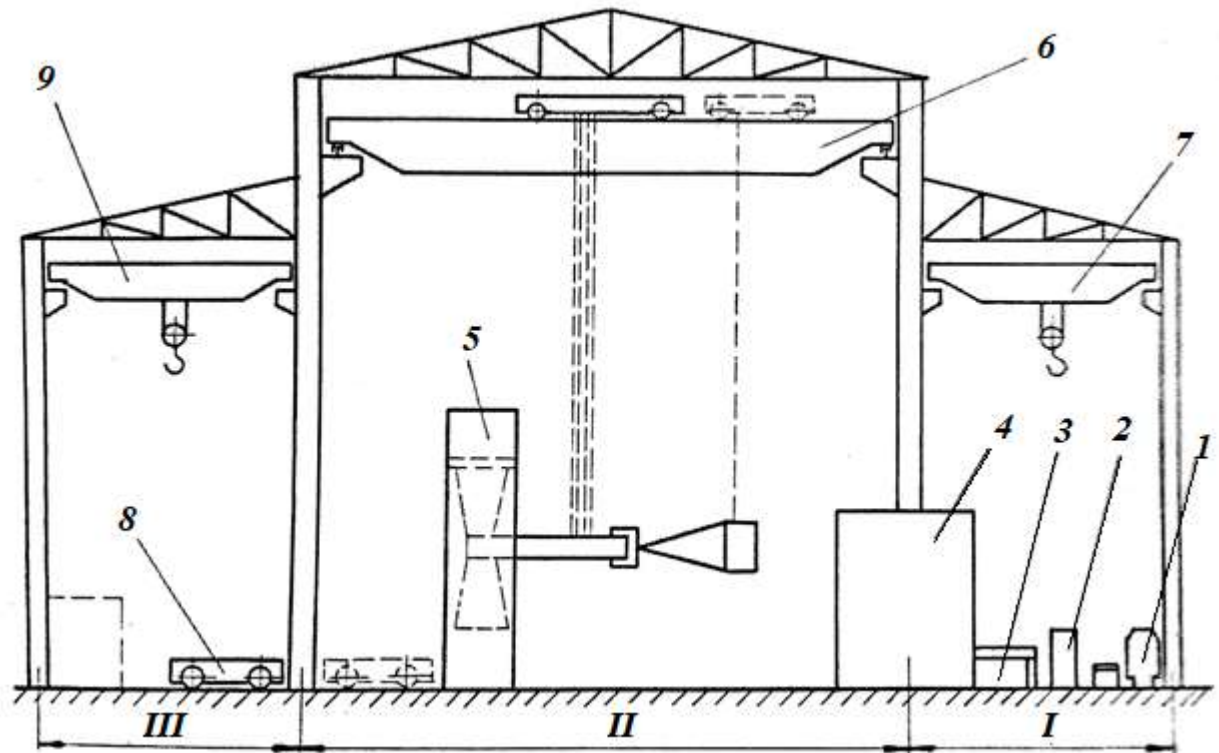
Механізація ковальсько-пресового цеху
